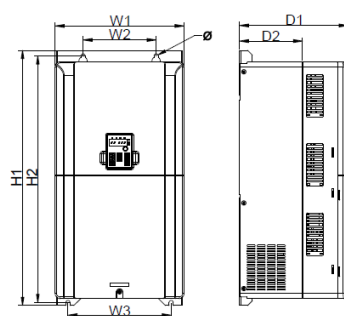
Настенный монтаж 45 – 75 кВт
